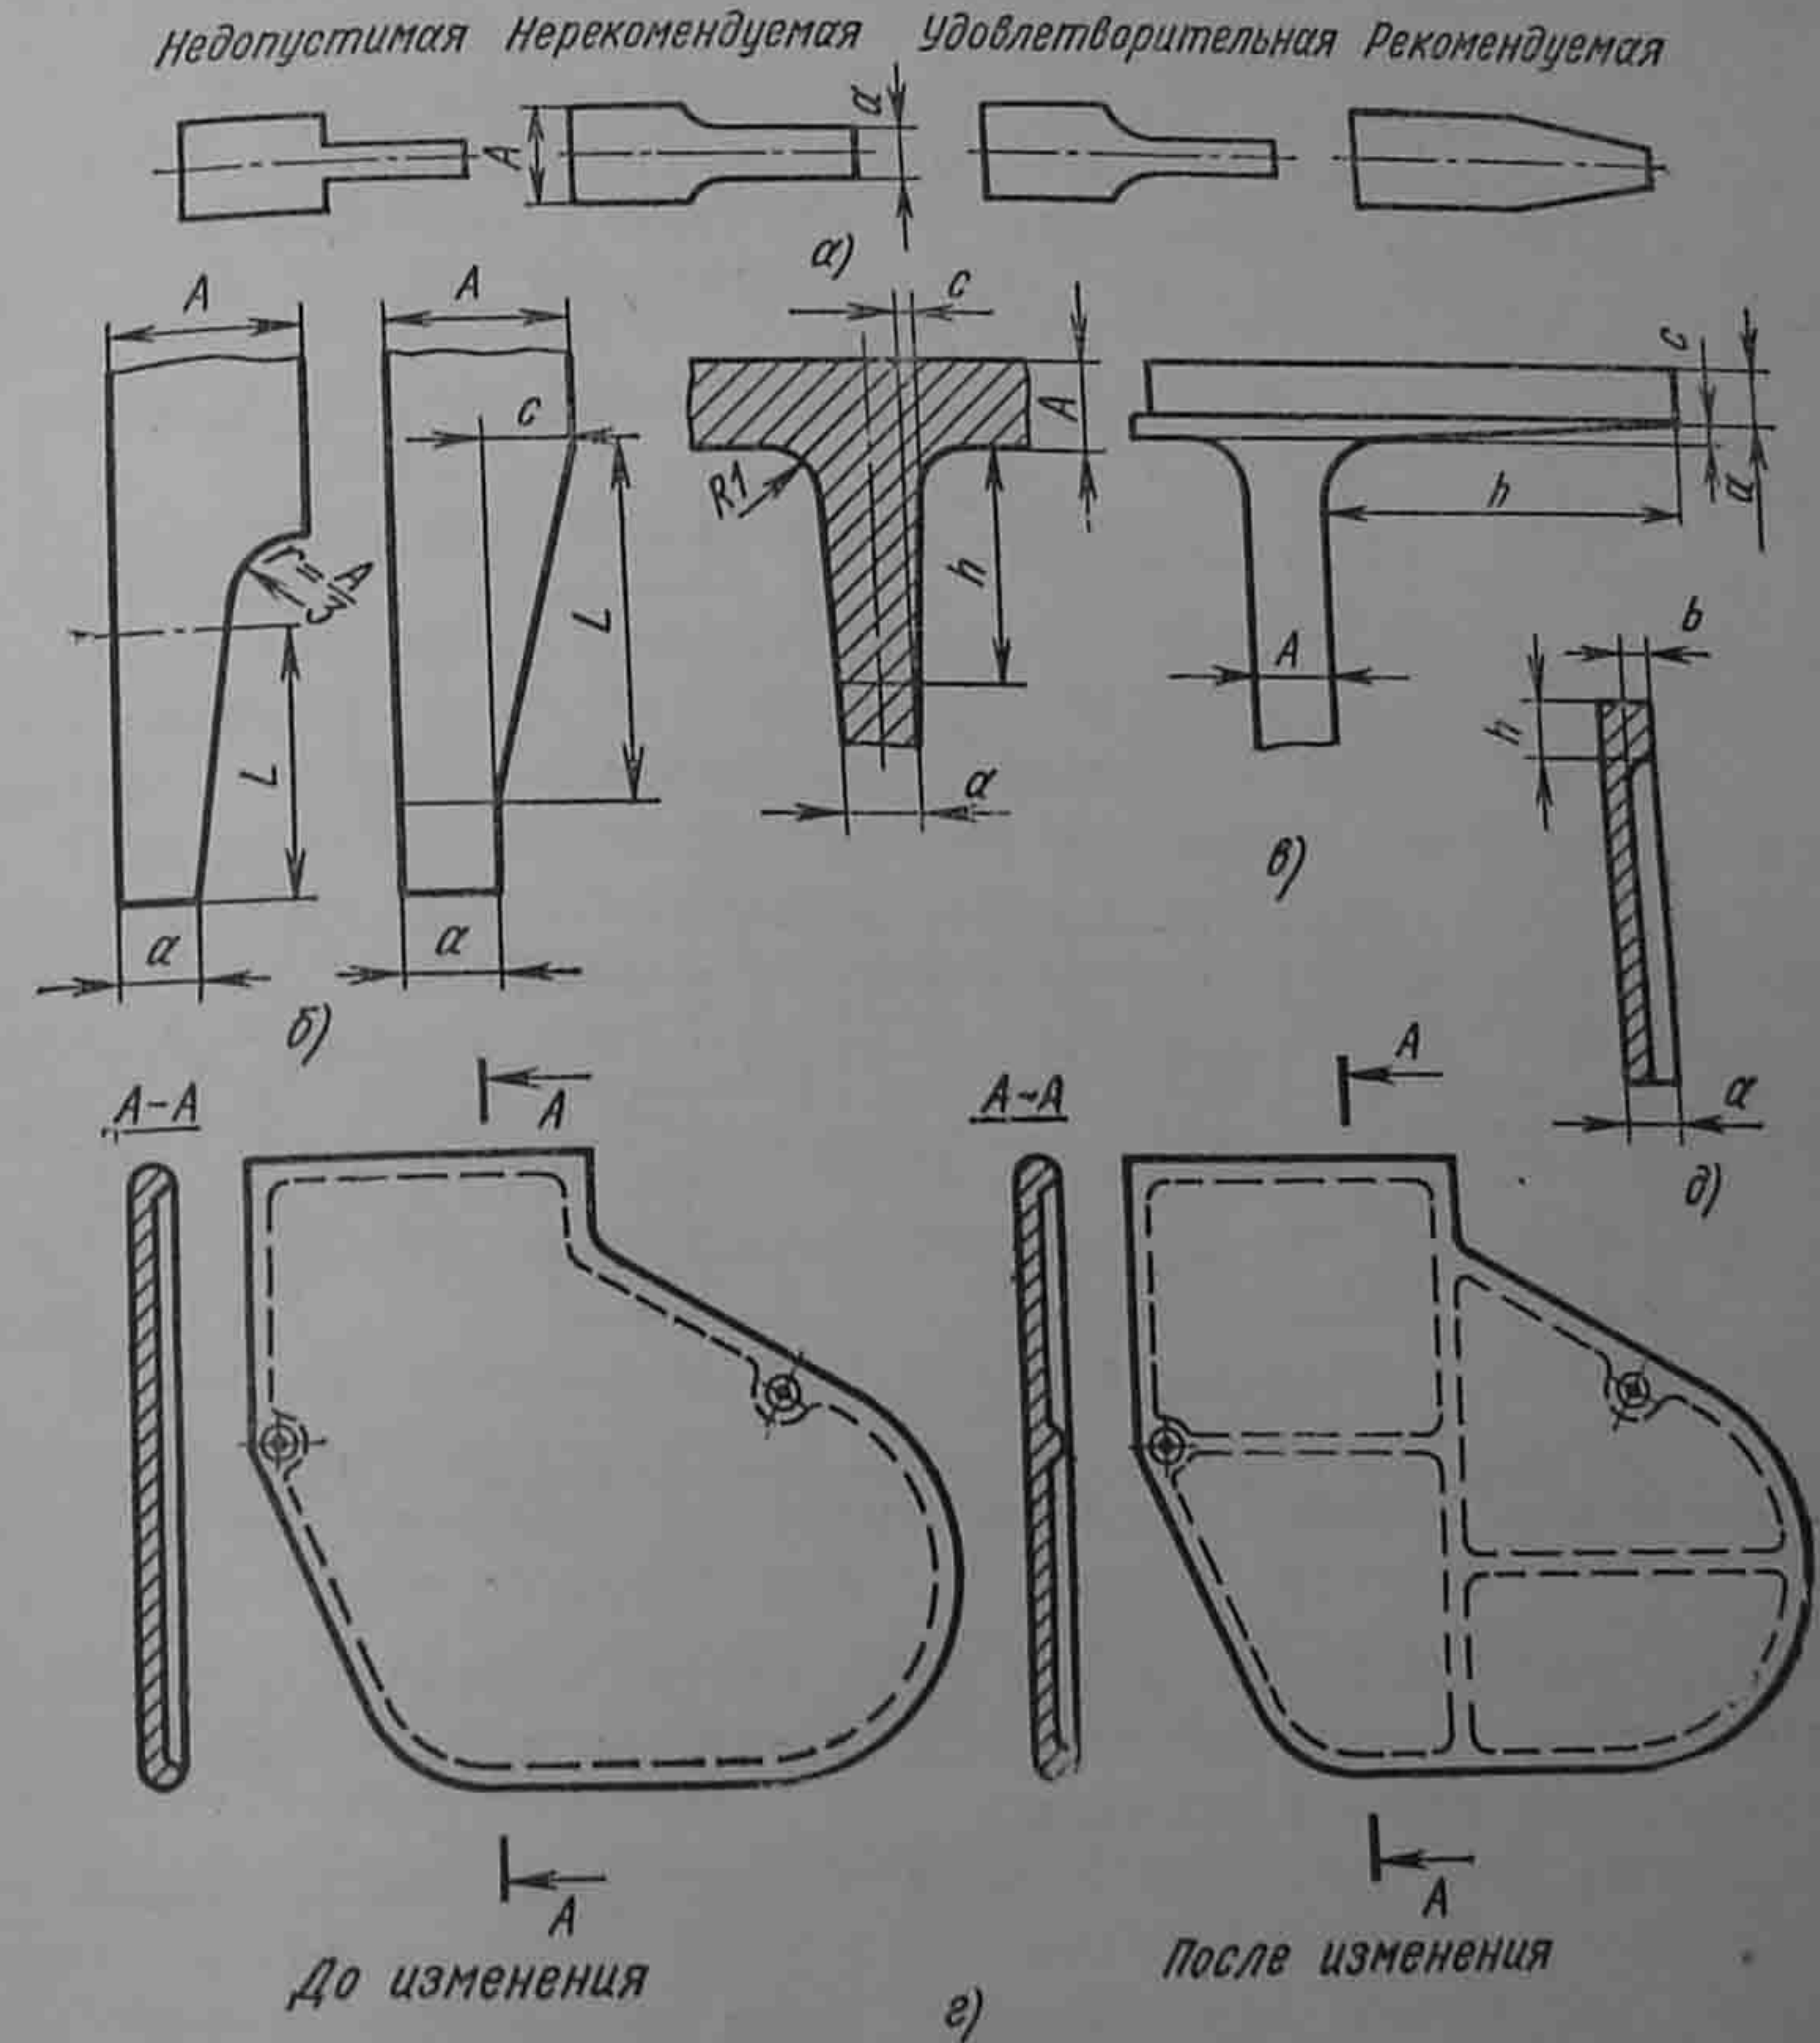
Конструктивные меры для предупреждения образования в отливке трещин и ее коробления
